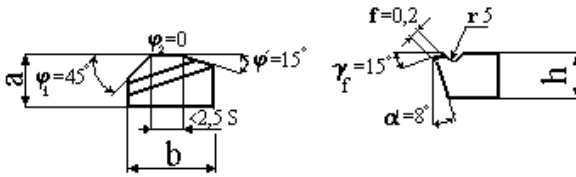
Розмір і геометрія ріжучої пластини
